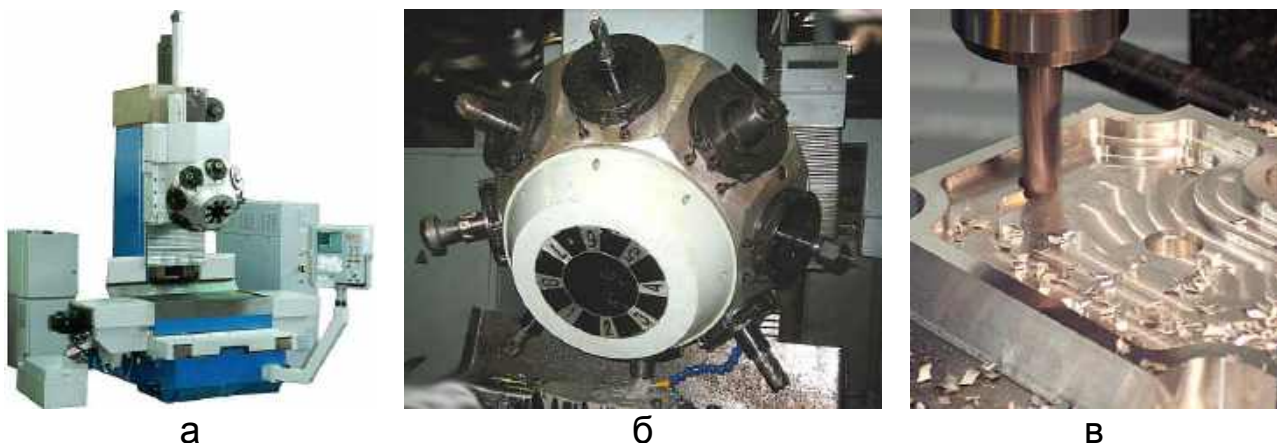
Вертикально-фрезерний верстат моделі MA-655CMH: а – загальний вигляд; б – корона заміни інструменту; в – приклад оброблення плити
